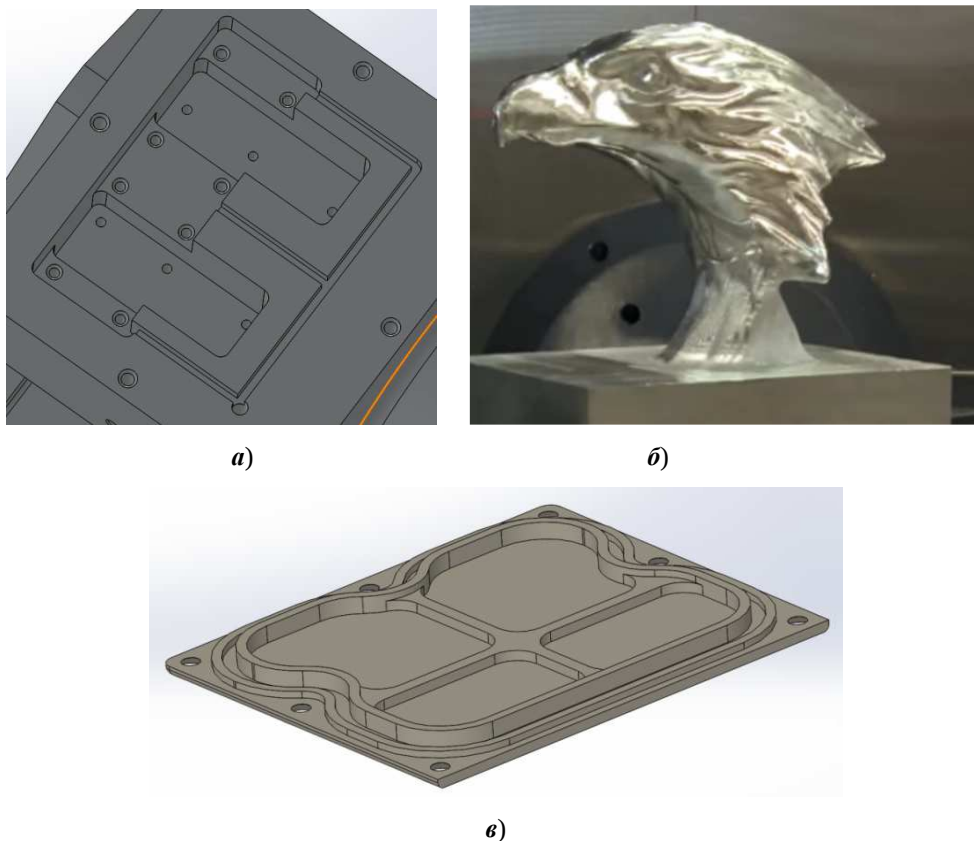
Примеры поверхностей, обрабатываемых на фрезерных станках с ЧПУ
